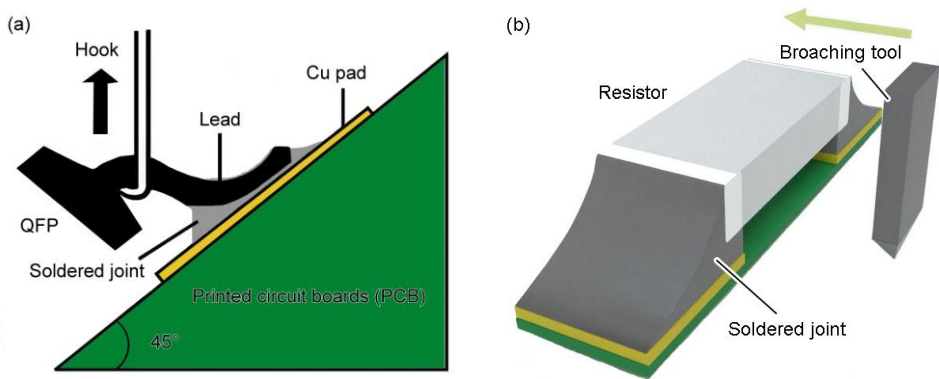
Sn-Ag-Cu 焊点的力学性能测试示意图
